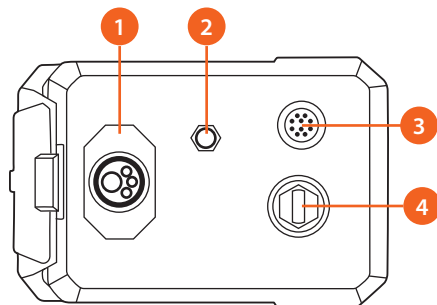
Механизм подачи проволоки – вид спереди
